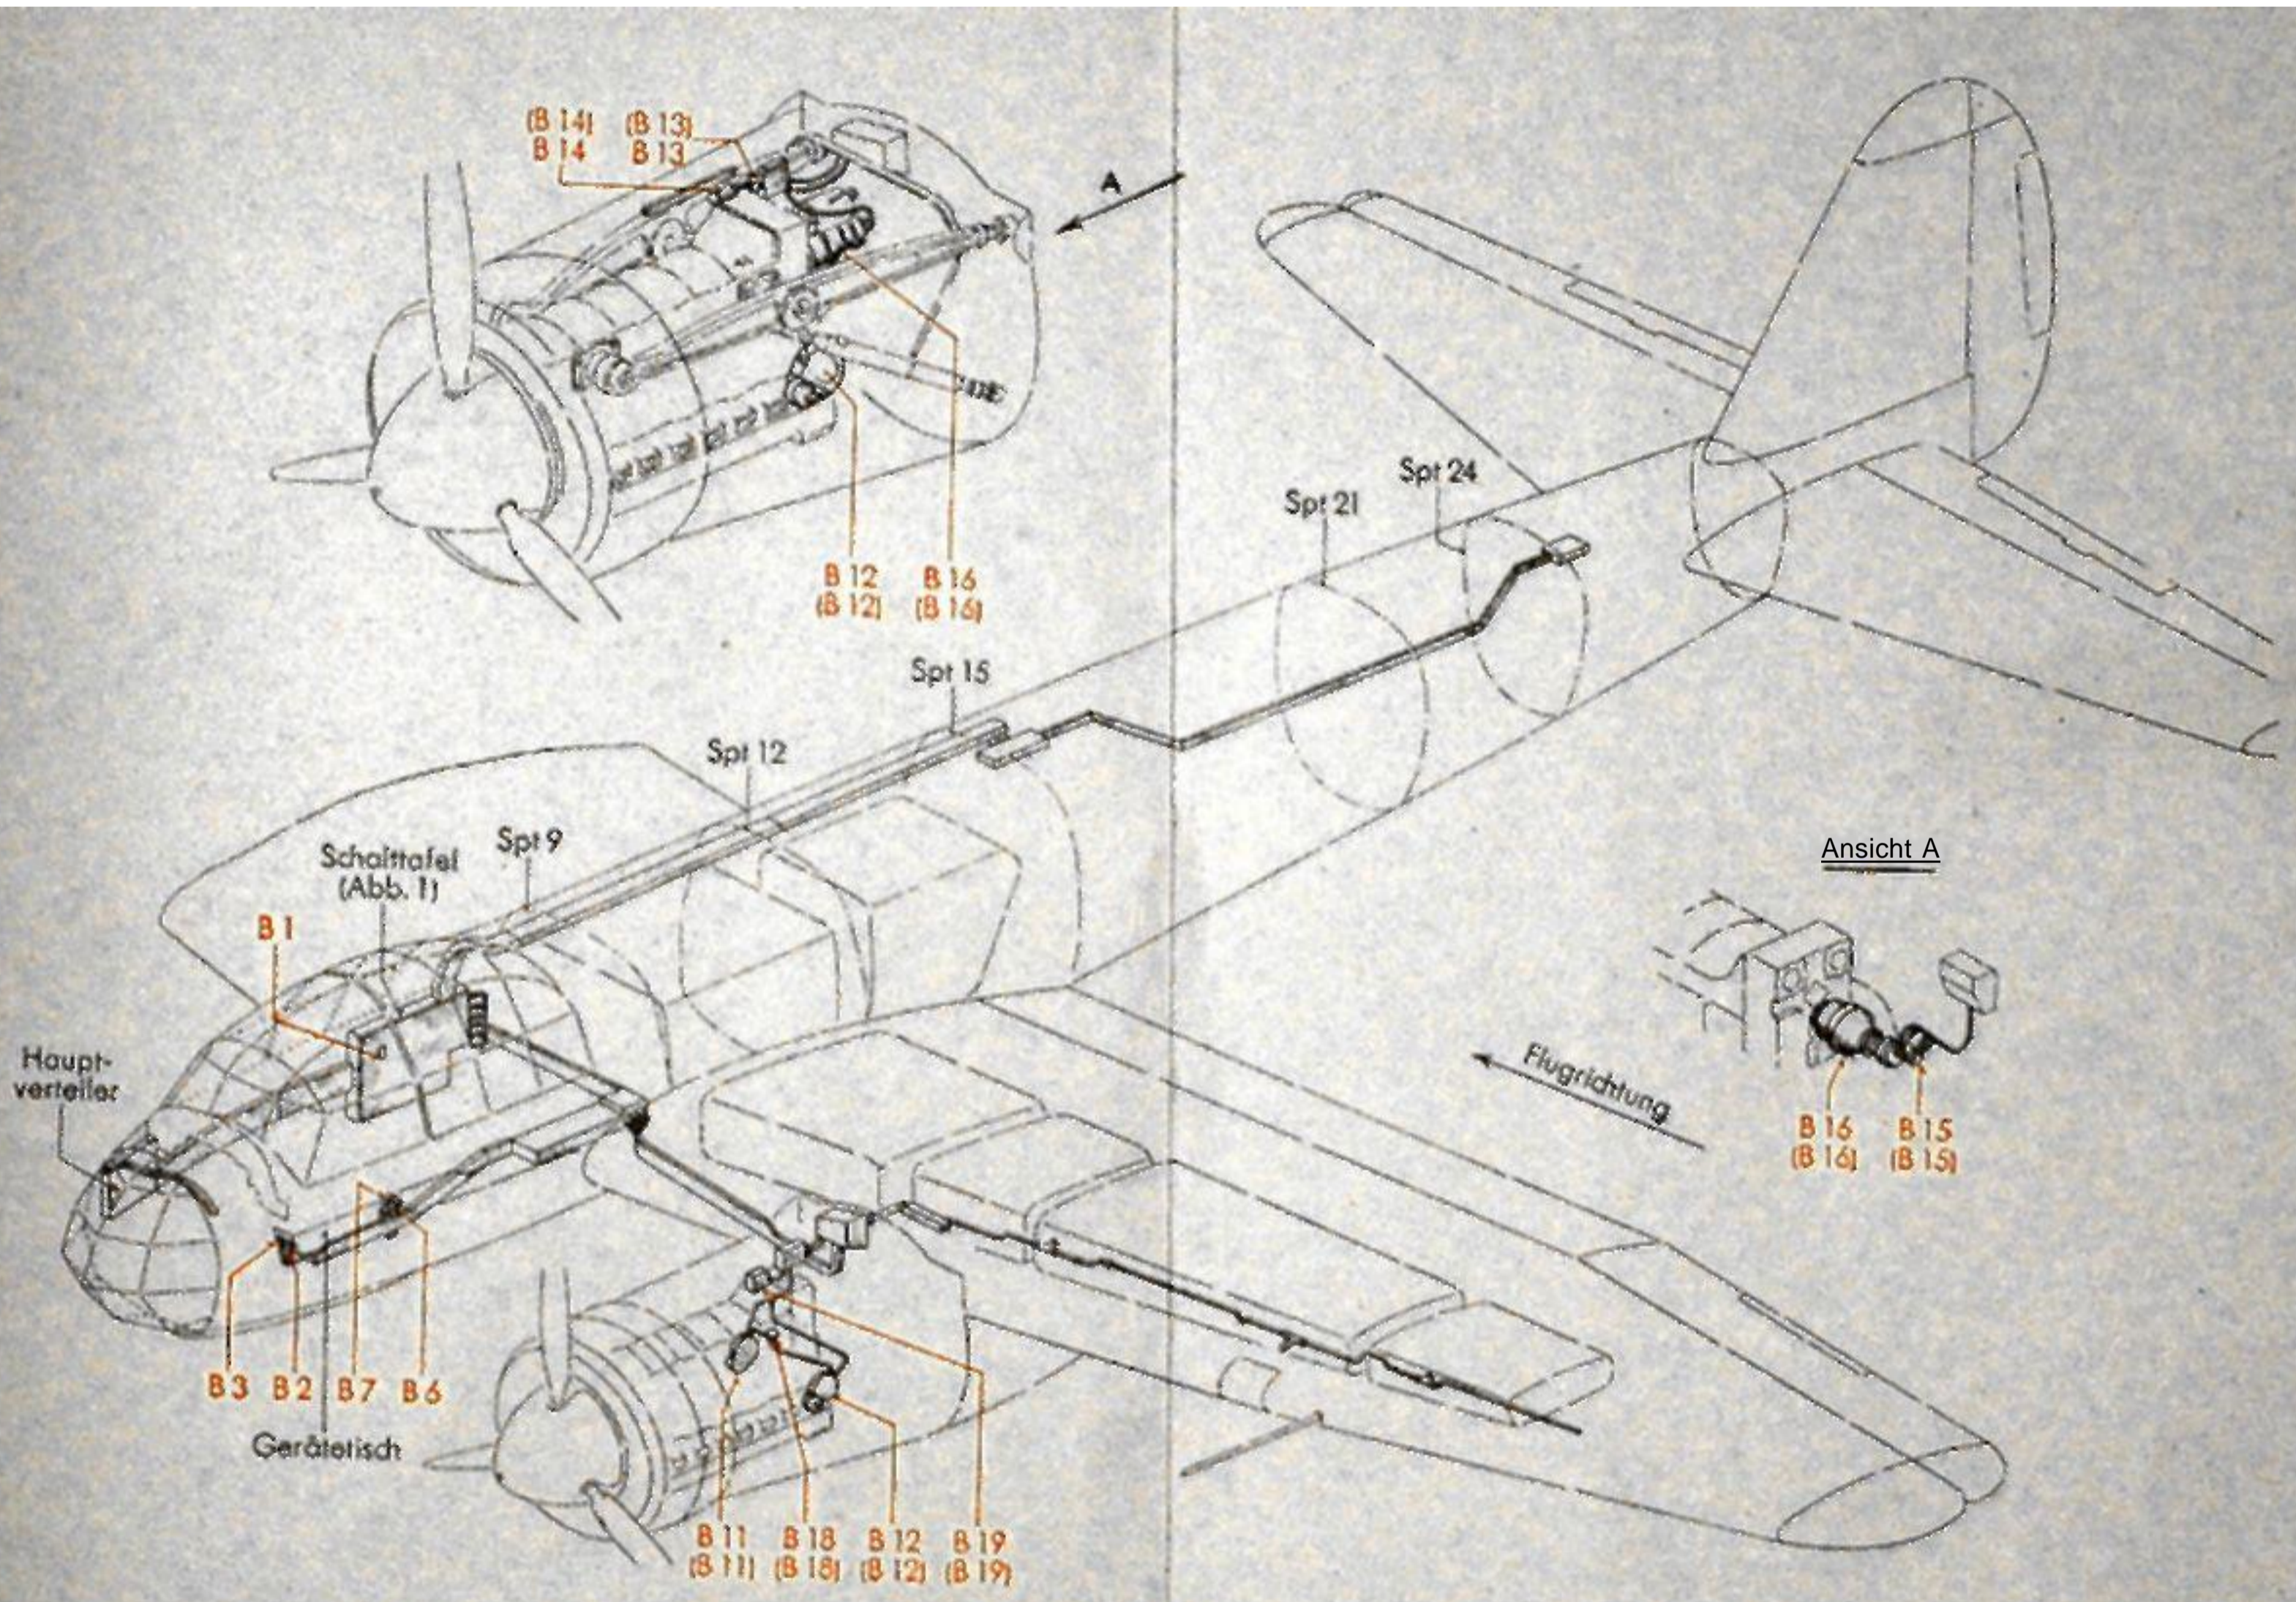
Lageplan der Anlaß- und Zündanlage / B-Anlage
